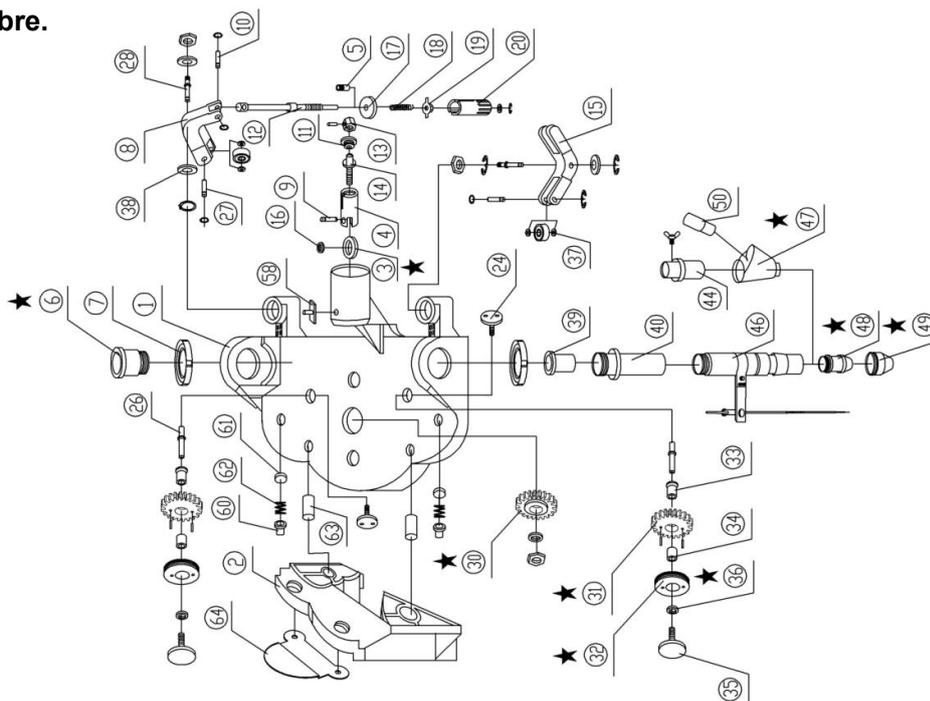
Desmontaje y montaje del soporte de la cabeza del tractor de un solo cable
